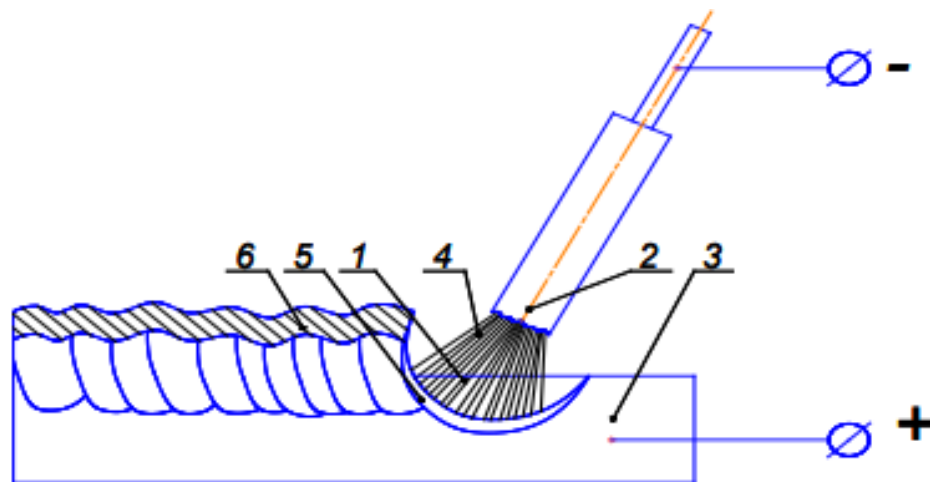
Ручне дугове зварювання: 1 – дуга; 2 – електрод; 3 – каплі; 4 – зварна ванна; 6 – шлакова кірка
